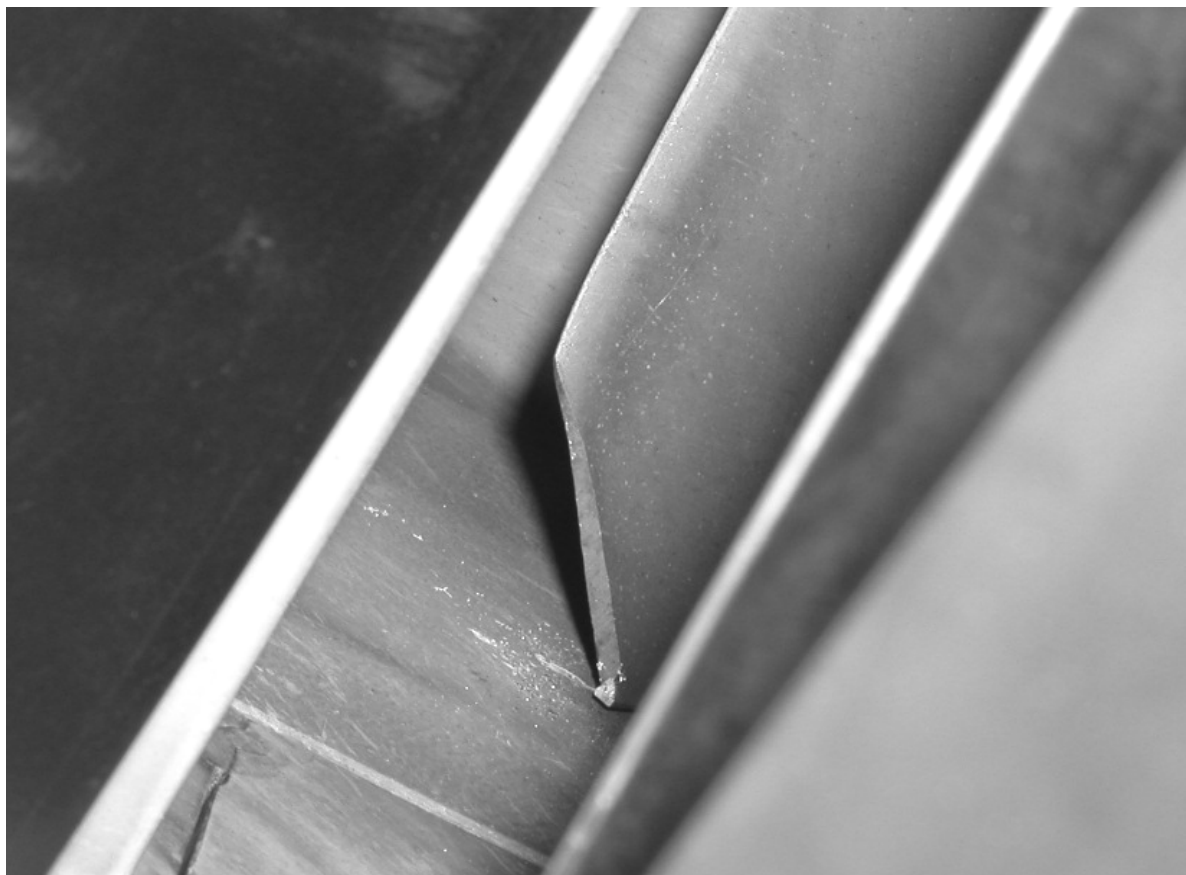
Рабочая лопатка второй ступени вентилятора двигателя Д-30КУ-154 с удалённым уголком
